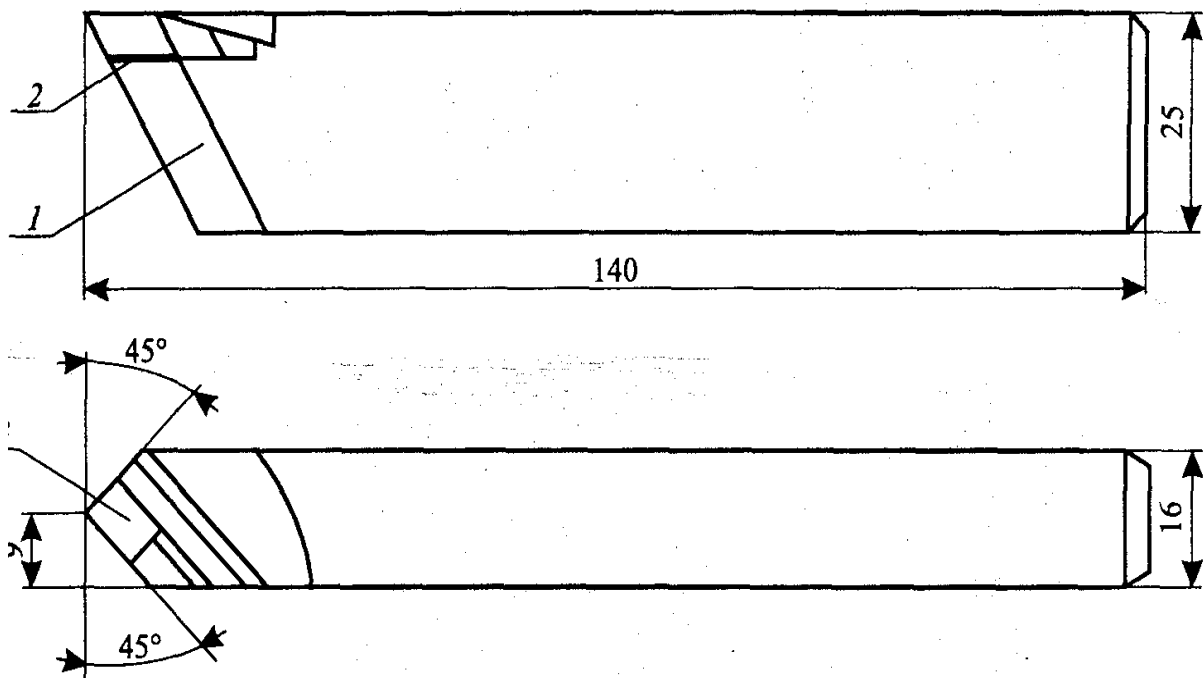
Різець з напаяною пластинкою (ТО А)
